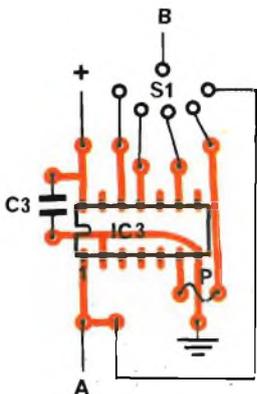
/B - Basetta vista dal lato componenti del selettore.
